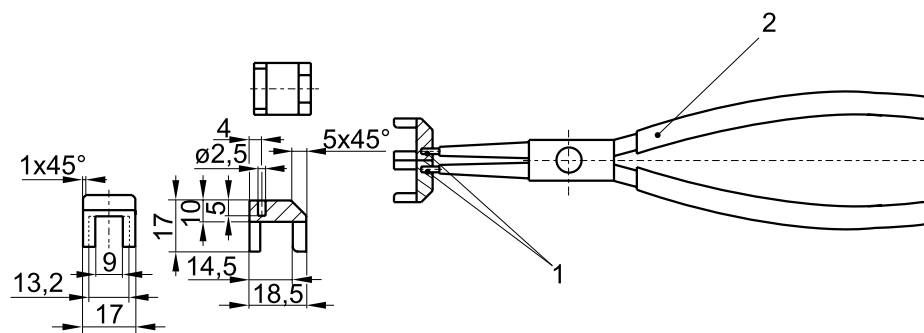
Werkzeug zum Einstecken der Kabelstecker für den Temperatursensor an den Kabelbaum
